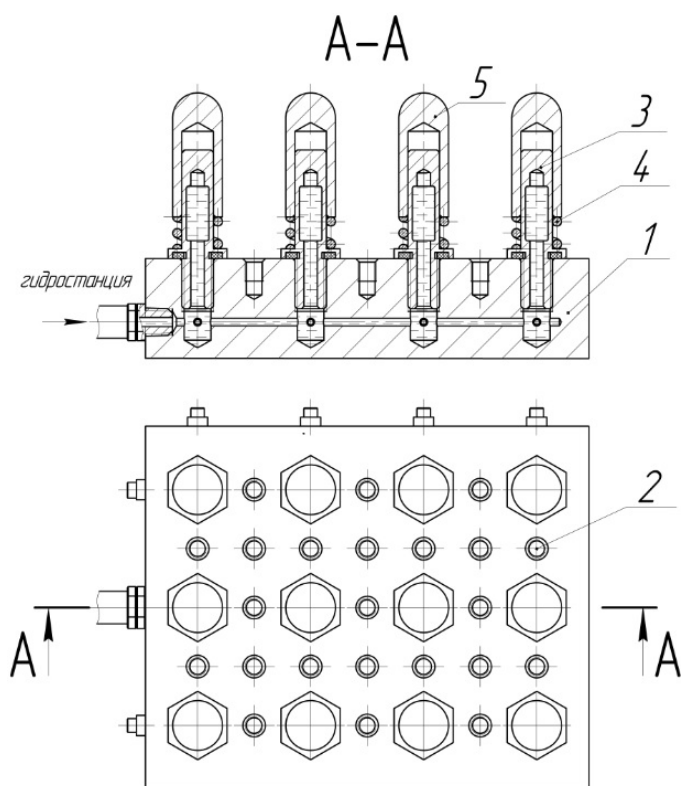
Приспособление с опорным модулем из самоустанавливающихся опор
